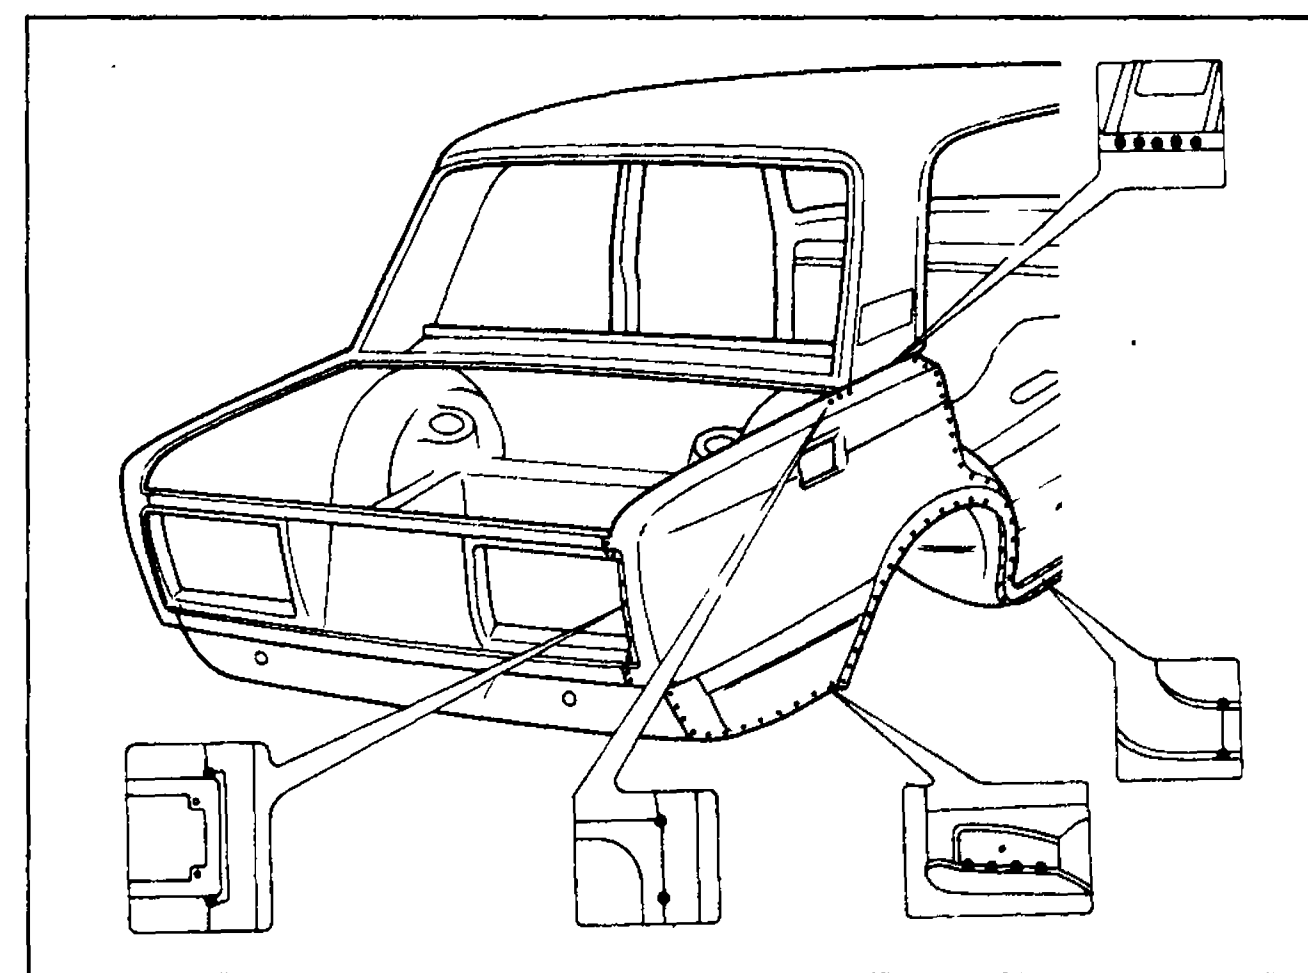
Места сварки заднего крыла. На основном виде точками обозначены швы контактной сварки. На фрагментах показаны места газовой сварки.
